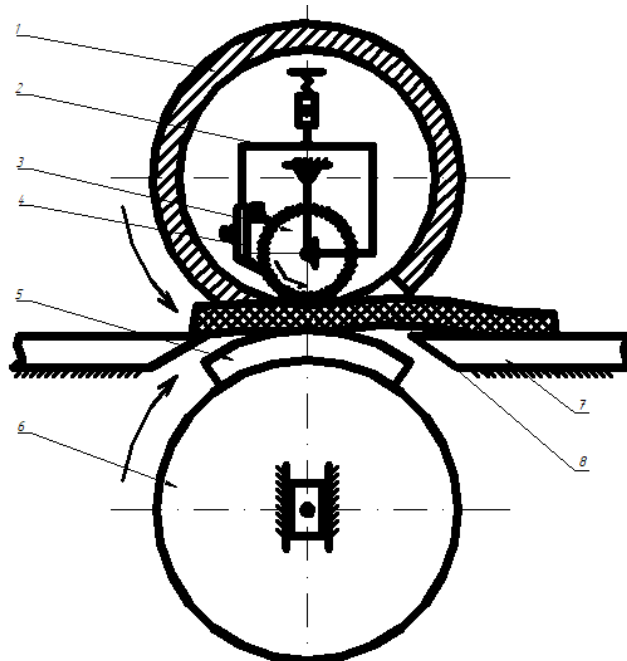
Пристрій для нанесення клею на ділянки деталей
